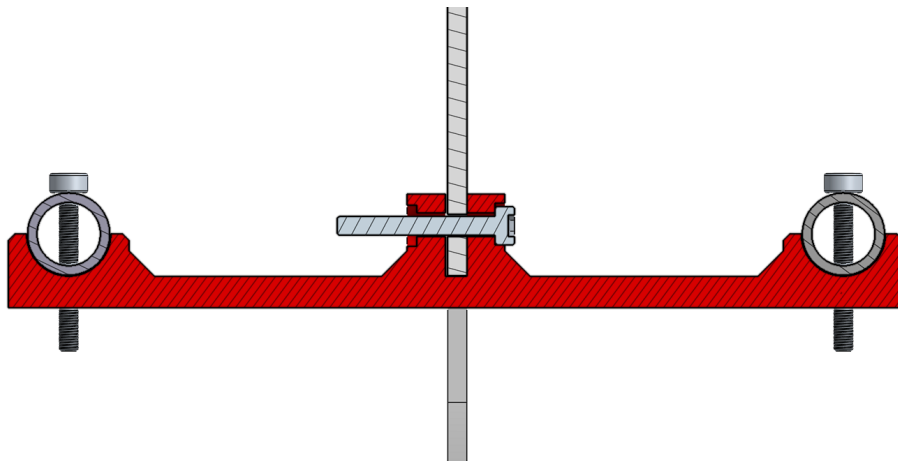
Vista frontal del ensamblaje de la estructura de la cola con vista de sección en Onshape [fuente: elaboración propia]
